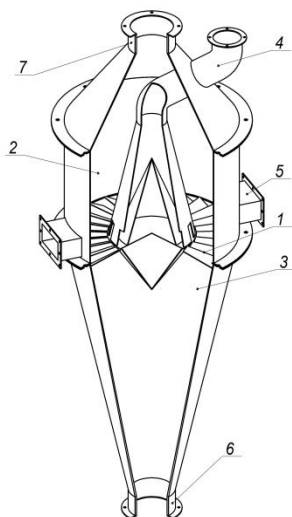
Схема сушильной установки: 1 – решетка газораспределительная; 2 – рабочая камера; 3 – газовая камера; 4 – загрузочный патрубок; 5 – разгрузочный патрубок; 6 – газоподводящий патрубок; 7 – газоотводящий патрубок
